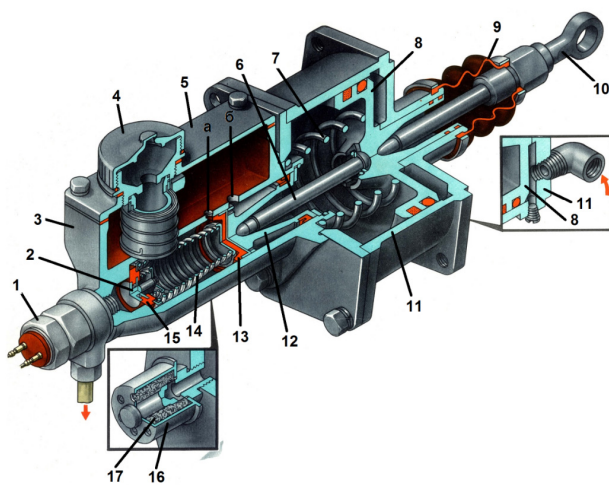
Главный цилиндр с пневмоусилителем:
